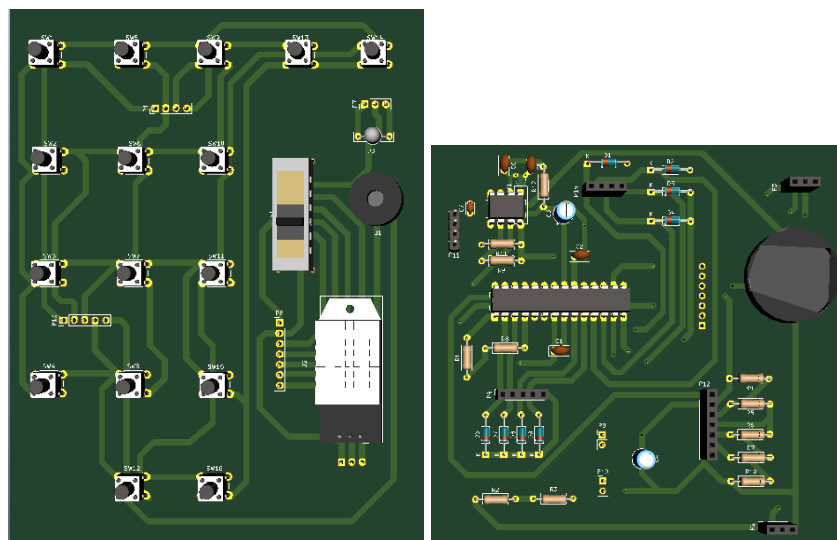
Diseño de las dos placas del dispositivo TSVR, realizado en KiCad.
